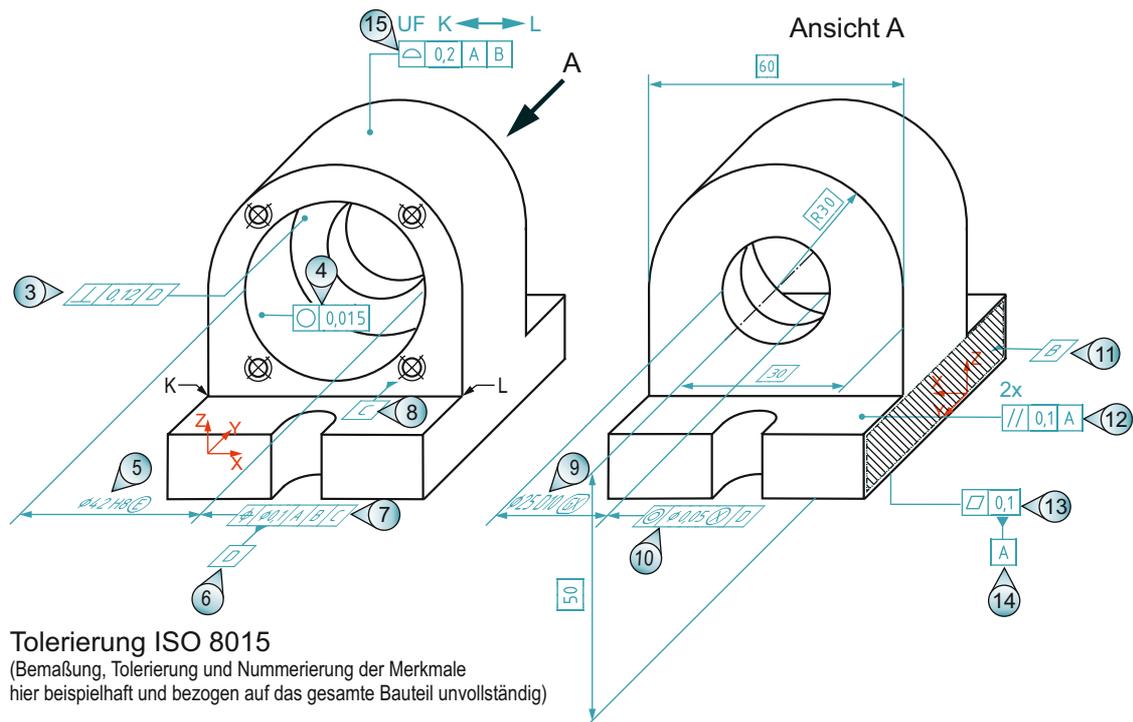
Bauteil Lagerbock – Ausschnitt aus der Zeichnung
